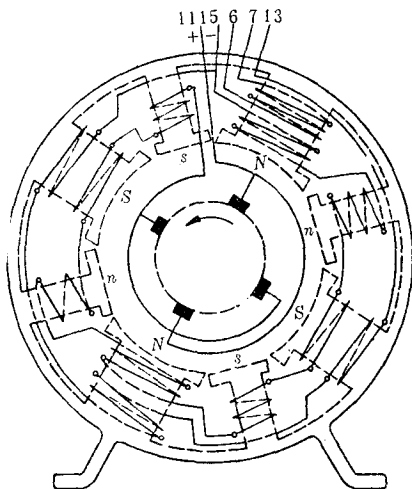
AX3-³⁰⁰/₅₀₀ 型焊接发电机的内部接线图（自换向器端视图）
